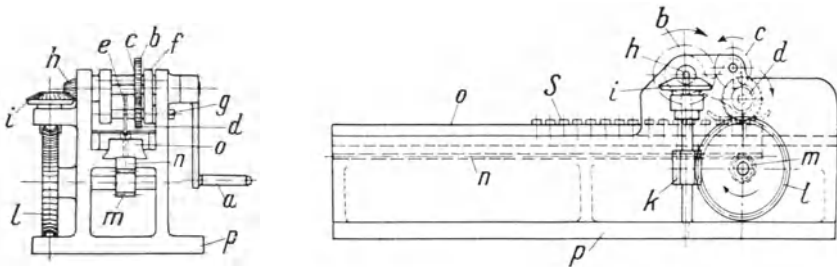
Hand-Schraubenschlitzvorrichtung für kleine Messingschraubchen.
